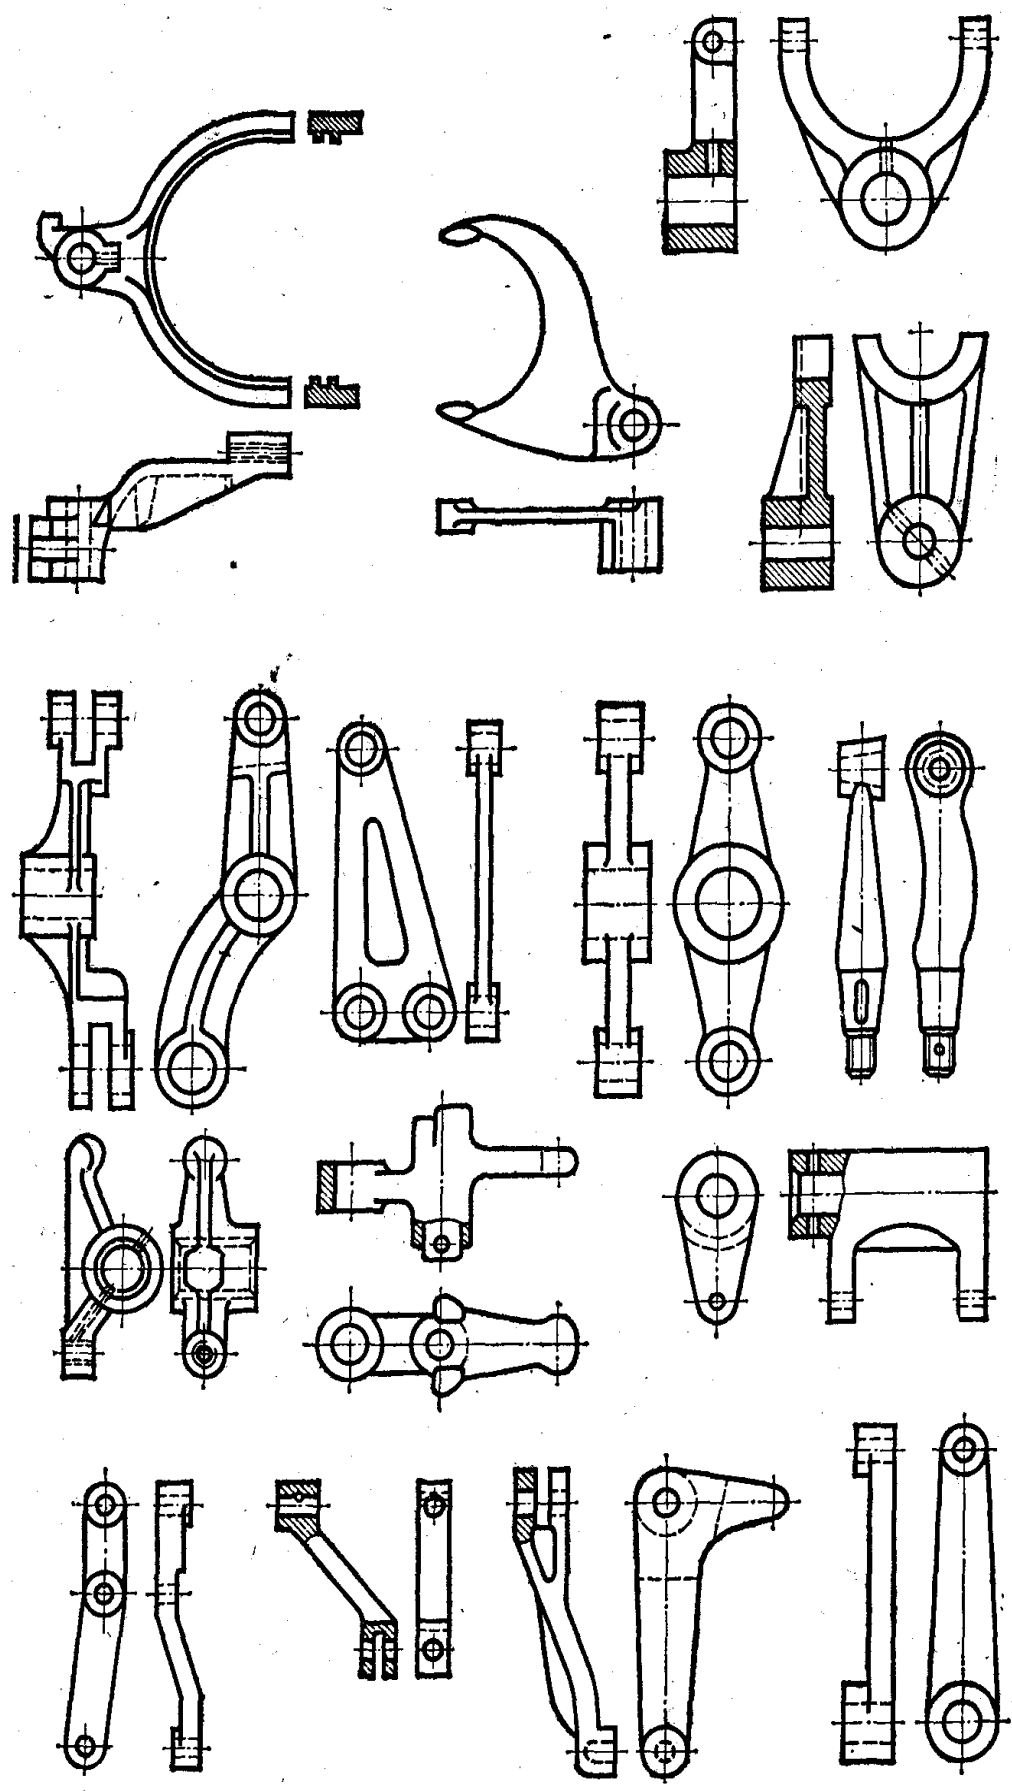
Конструктивные разновидности деталей класса рычагов
